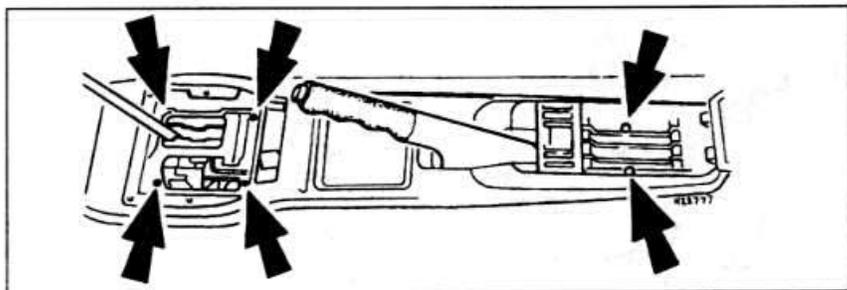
Расположение гаек и винтов крепления центральной консоли с автоматической коробкой передач.
